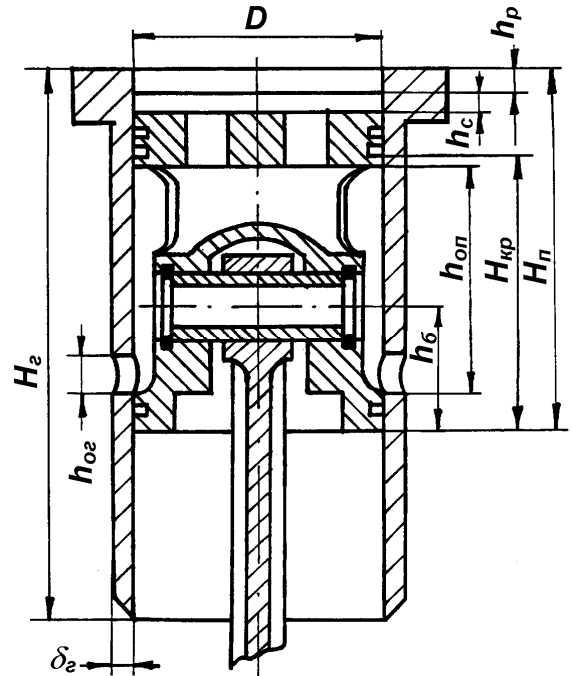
Шатунно-поршнева група прямоточного компресора
